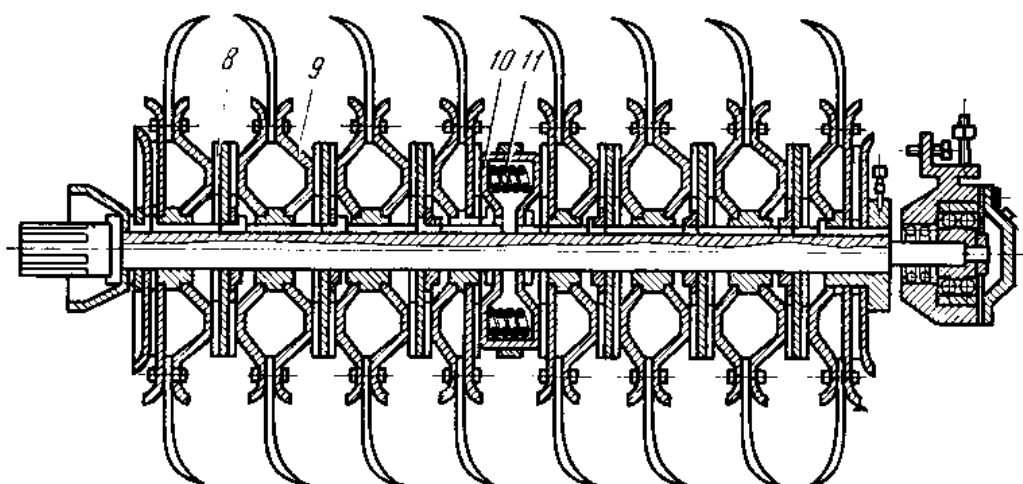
Общий вид фрезерного барабана болотной фрезы ФБН-0,9:
